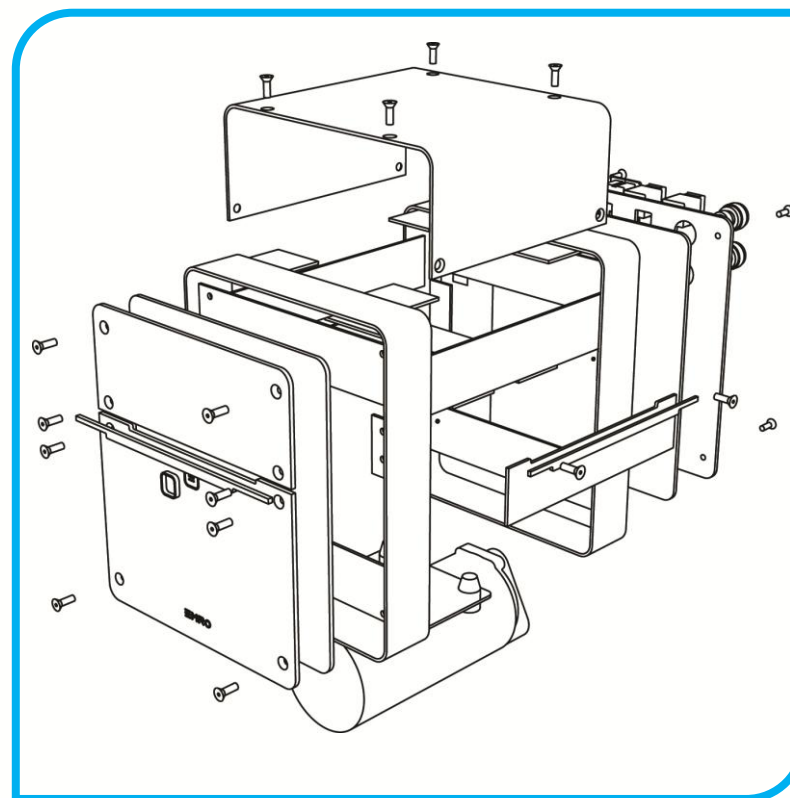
Despiece Módulo de bomba. Fuente: elaboración propia
